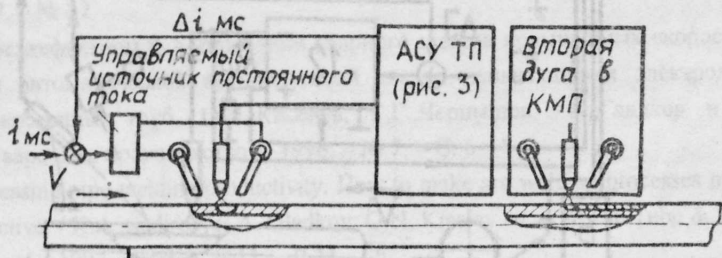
АСУ ТП двухдуговой сварки с внешним КМП на двух дугах (управление внешней формой шва, проплавлением и величиной гребта в шве)
